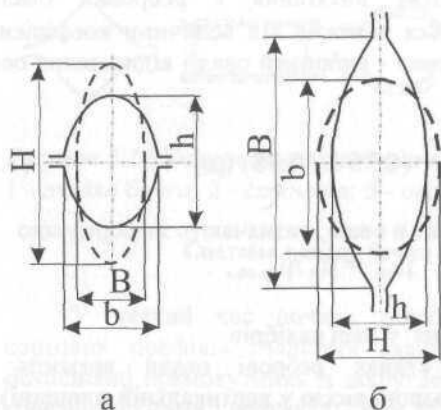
Система калібрів: а - овал - ребровий овал; б - ребровий овал-овал
